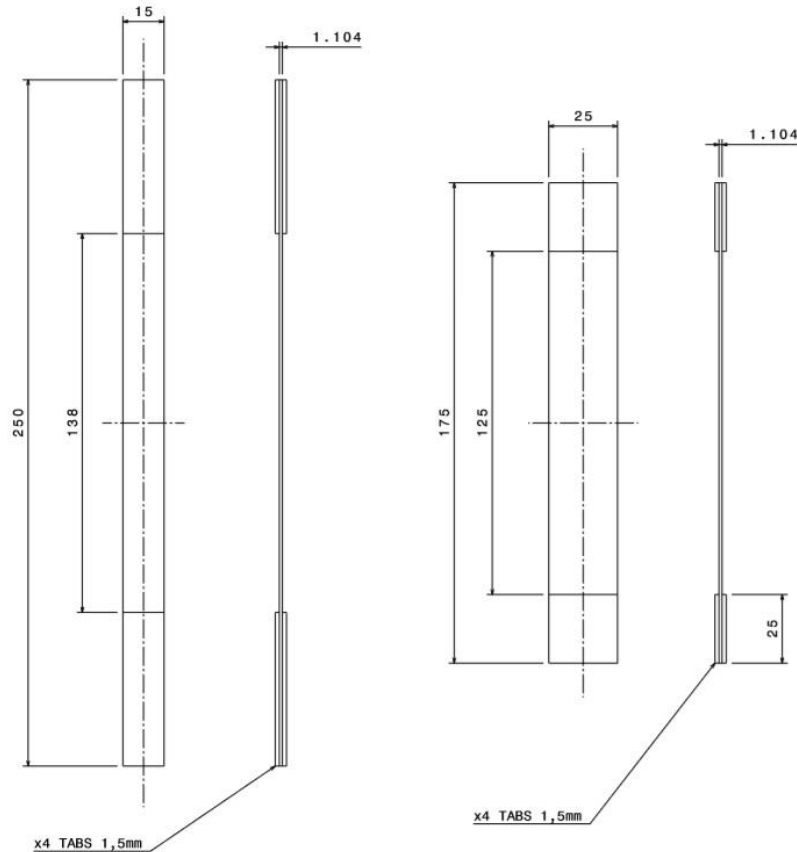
Planos de la probeta de tracción 0° (izquierda) y 90° (derecha)
